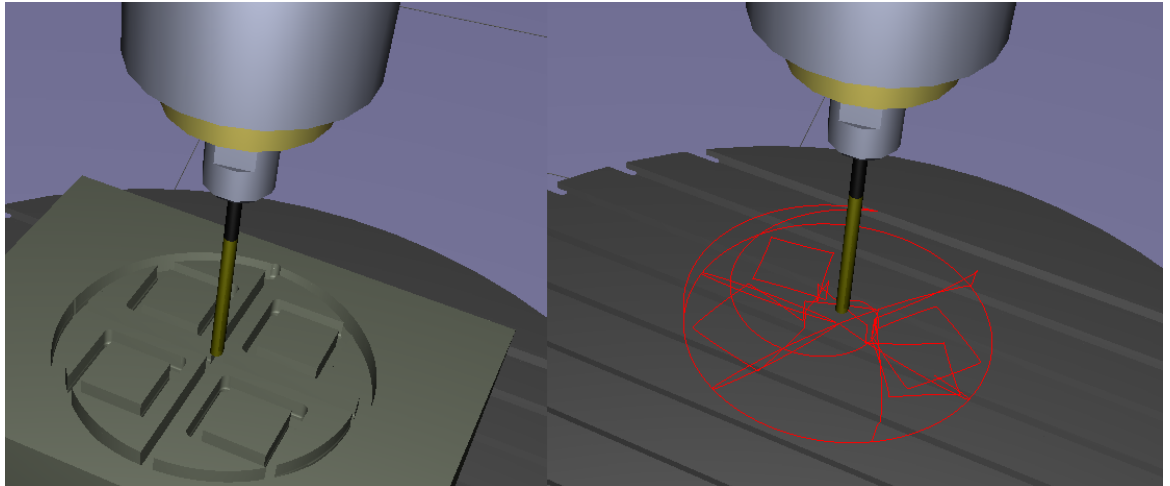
Bearbeitetes Werkstück (links) während einer Drehung, rechts die Traceansicht
